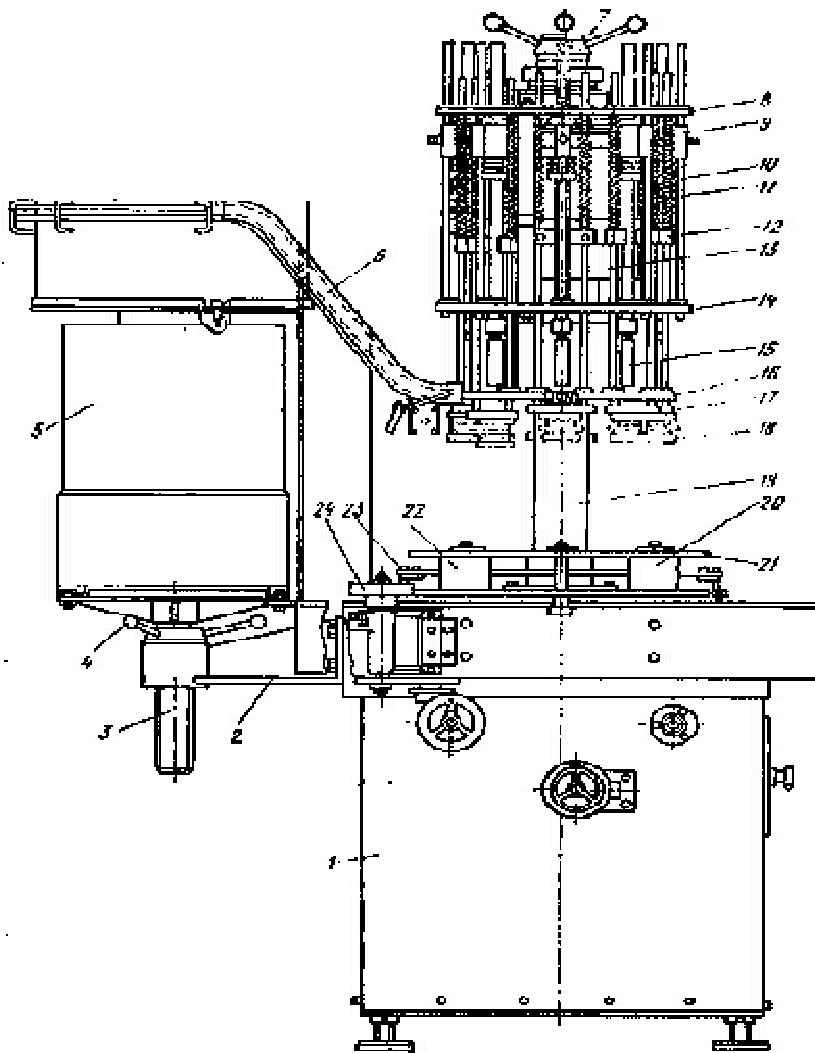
Закупорювальна машина ВРО/2 (загальний вигляд): 1 - станина; 2 - кронштейн; 3 - гвинт; 4, 7 - гайки-маховики; 5 - вібробункер; 6 - пробкопровод; 8, 14, 16 - диски; 9 - обойма; 10, 13 - напрямні; 11 - пружина; 12
